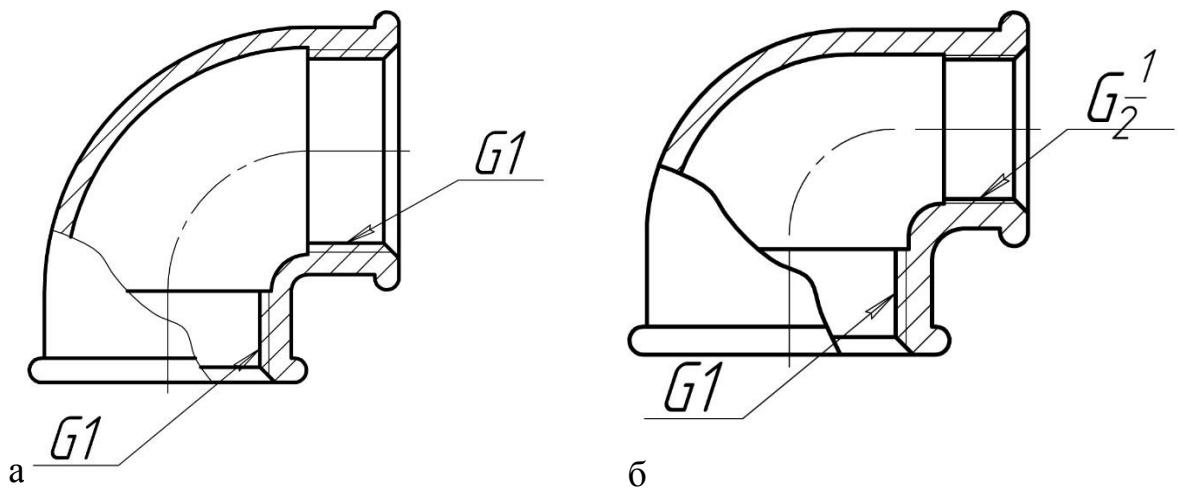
Соединительные части из ковкого чугуна для соединения труб под углом:
